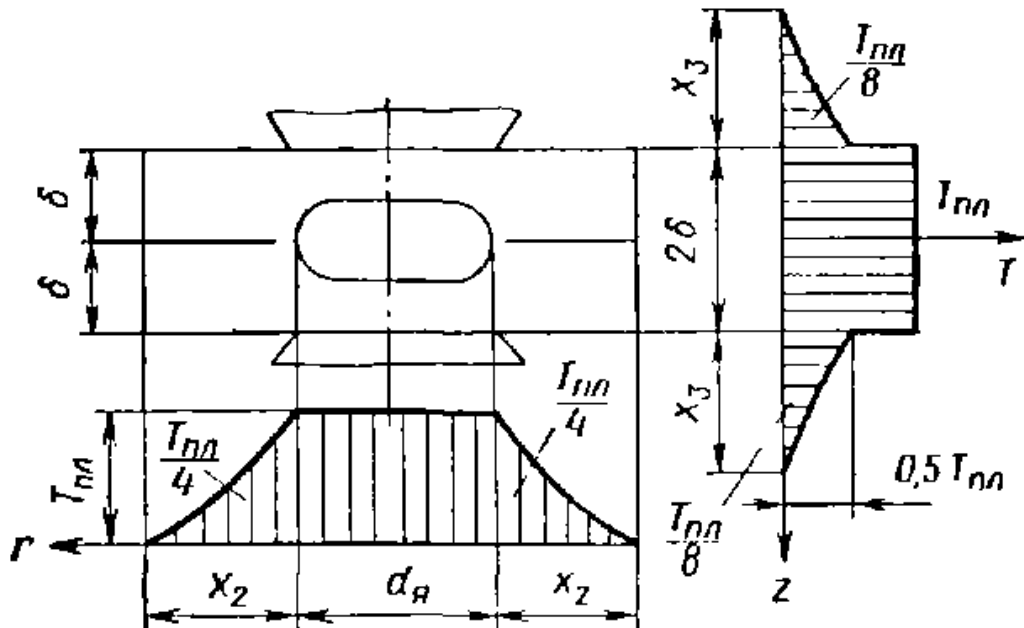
Схема расчета действующего значения сварочного тока при точечной сварке
